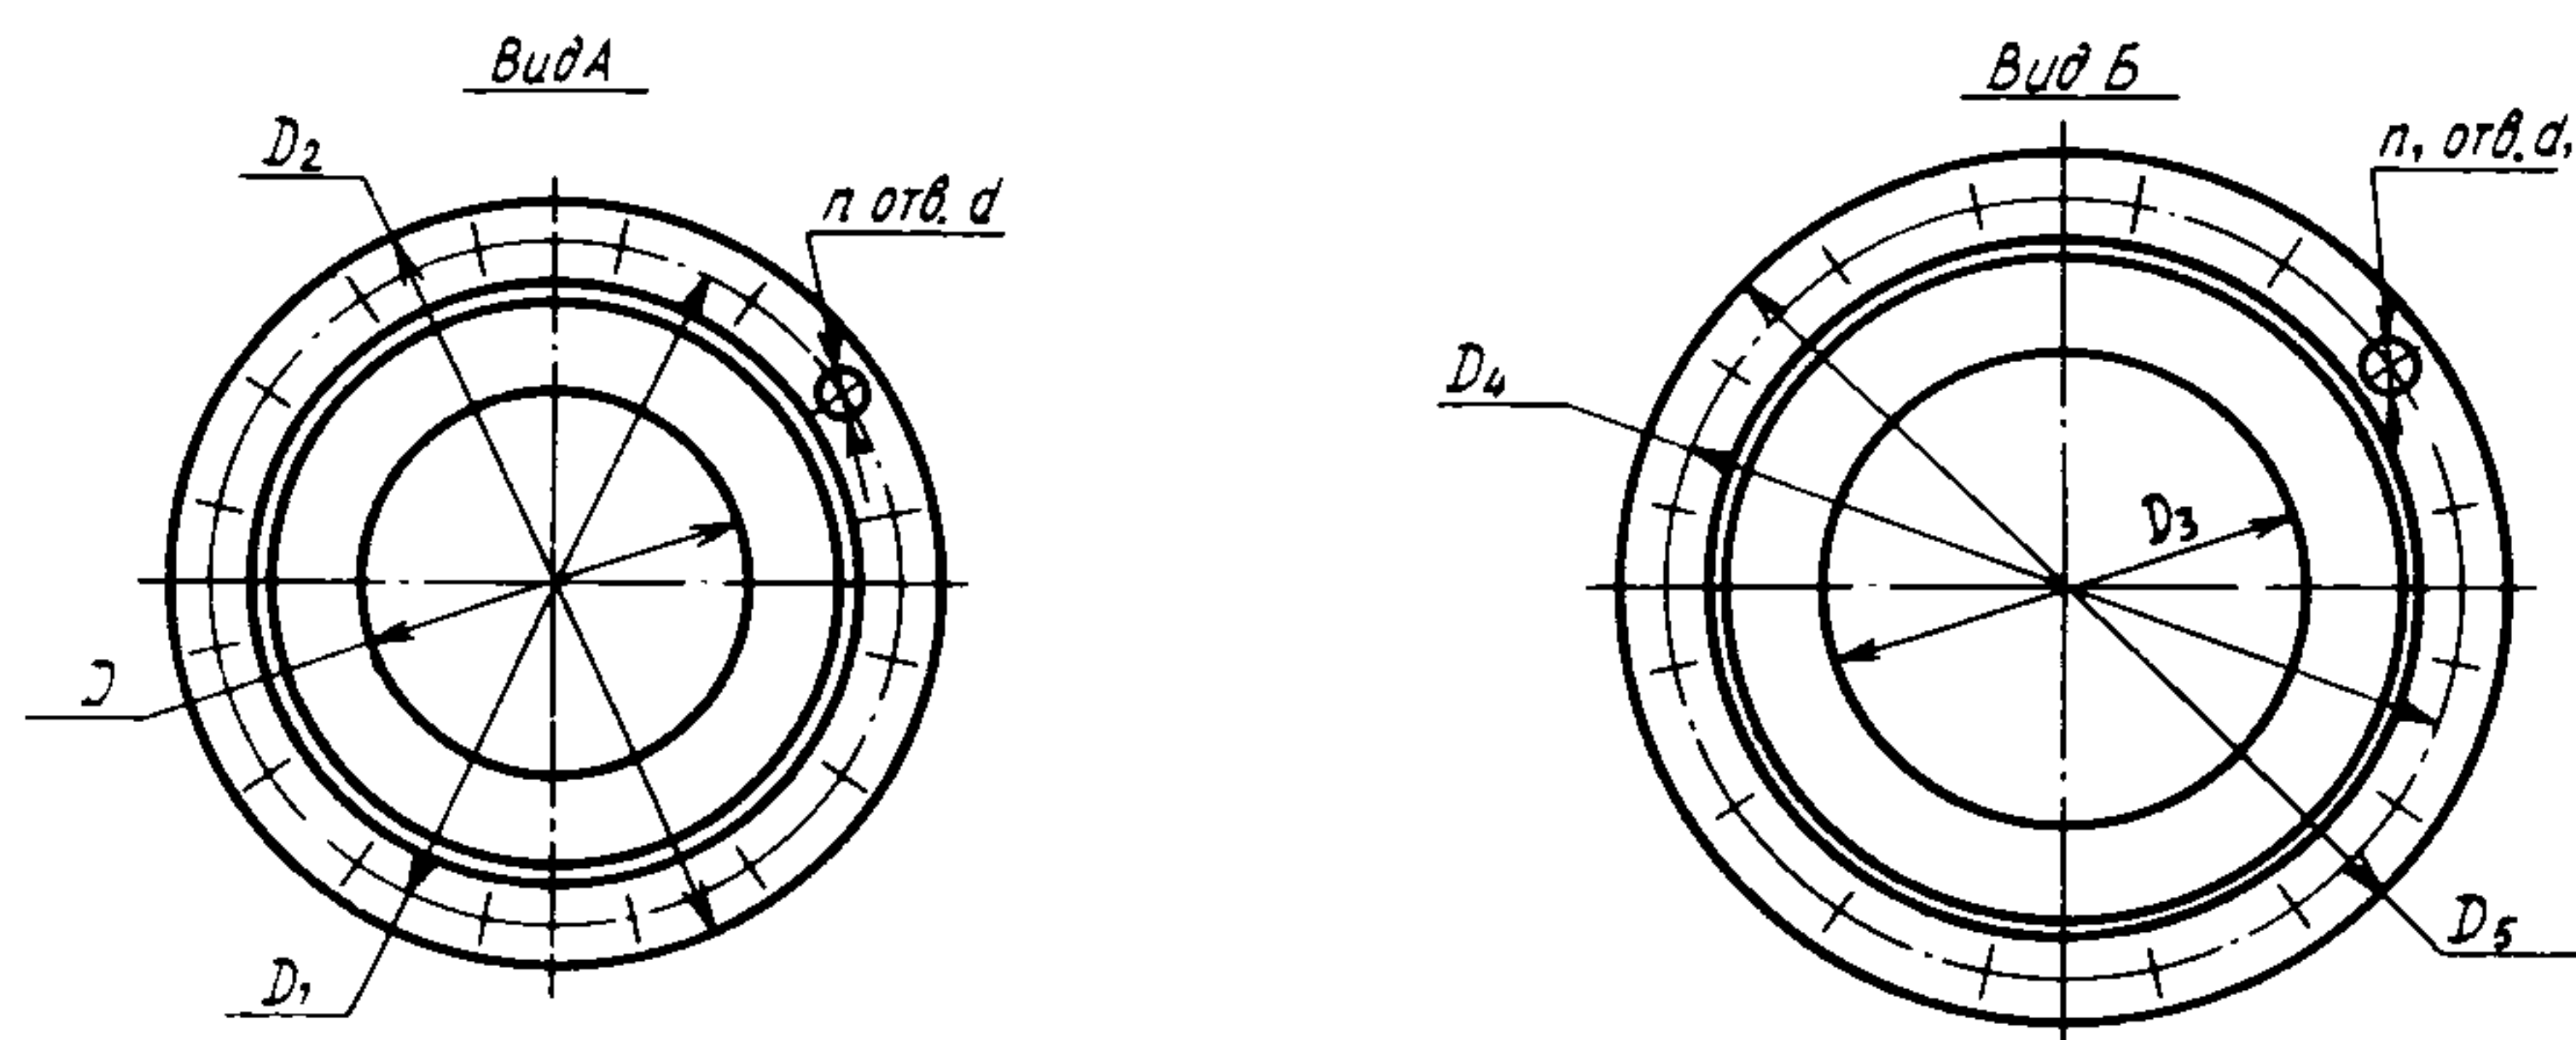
Присоединительные размеры патрубков насосов типа ГрА
